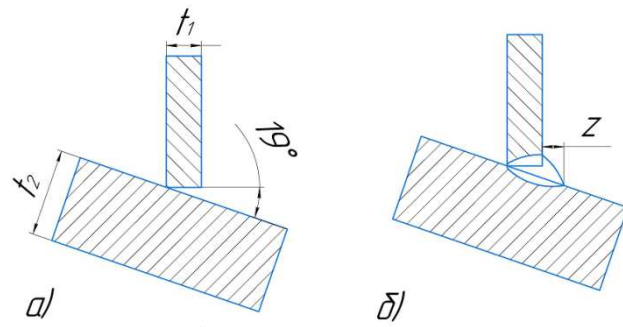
З'єднання № 1 а) – складання, б-зварне з'єднання Т1 (ГОСТ 23518-79)
